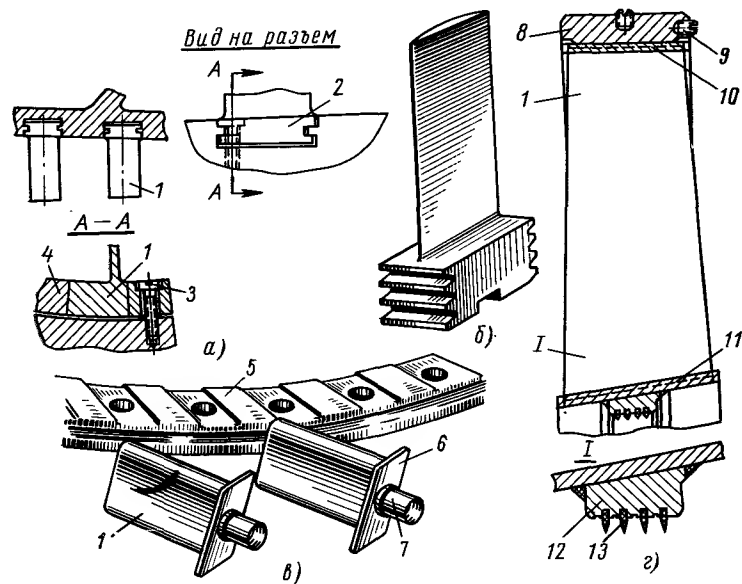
Детали направляющих аппаратов осевых компрессоров: а — ГТ-700-5 НЗЛ; б — ГТУ L-51С компании АЕИ; в — ГТУ G-9 Народных предприятий ГДР; г — ГТУ мощностью 50000 кВт; 1 — направляющая лопатка; 2 — концевая вставка; 3 — стопорный винт концевой вставки; 4 — промежуточная вставка; 5 — полукольцо; 6 — полка; 7 — цапфа; 8 — внешнее полукольцо; 9 — штифт; 10 и 11 — бандаж; 12 — внутреннее кольцо; 13 — усики лабиринтного уплотнения
